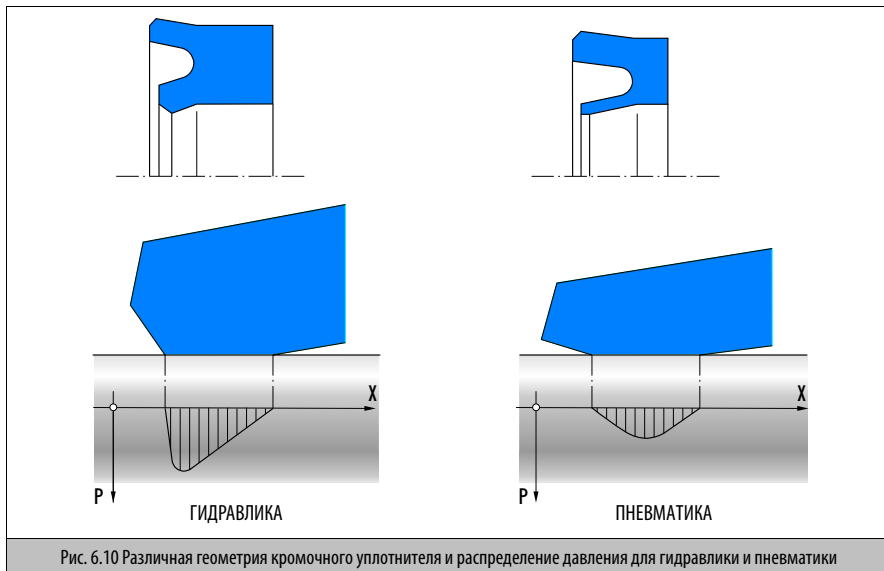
Различная геометрия кромочного уплотнителя и распределение давления для гидравлики и пневматики
